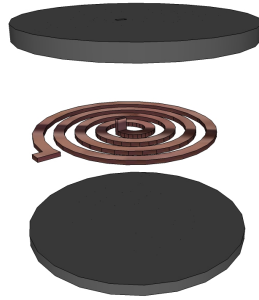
Vue éclatée d'une inductance monolithique cofrittée par le procédé PECS de diamètre 20 mm et d'épaisseur 3 mm[Bea11].
